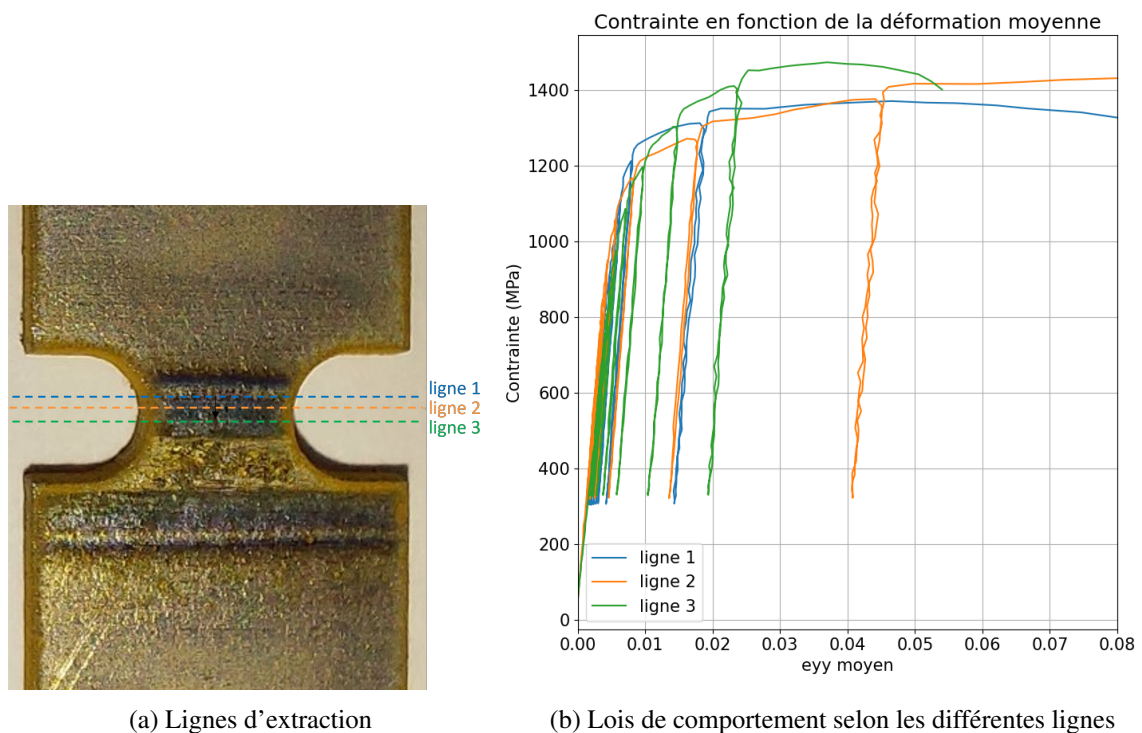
Lois de comportement dans la largeur de la ZAT - éprouvettes à encoches larges avec soudure
